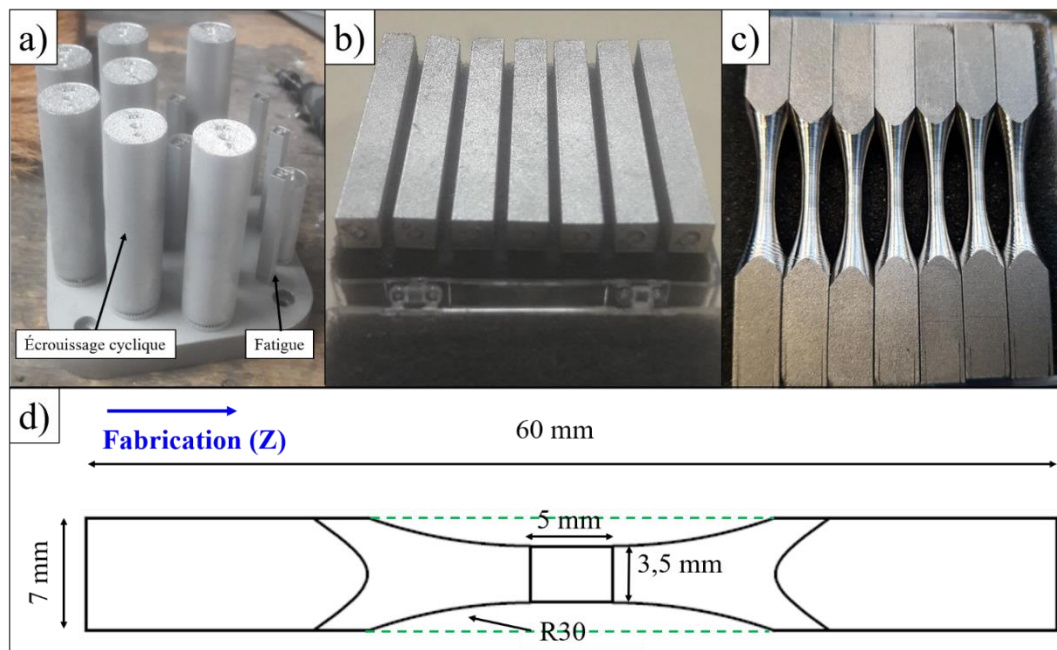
a) b) Cylindres pour écouissage cyclique et parallélépipèdes bruts de fabrication c) Éprouvettes SI-1 à SI-7 après usinage d) Modèle d'éprouvette fabriqué. Les pointillés verts délimitent les bords du parallélépipède rectangle avant usinage
